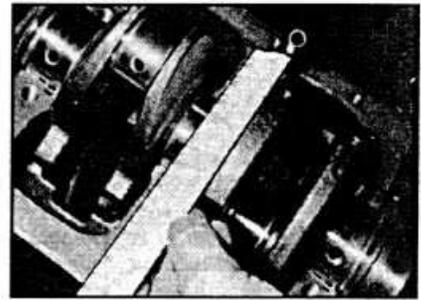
Е.30. Измерение деформации измерительного стержня Plastigage для определения зазора в коренном подшипнике коленчатого вала.
